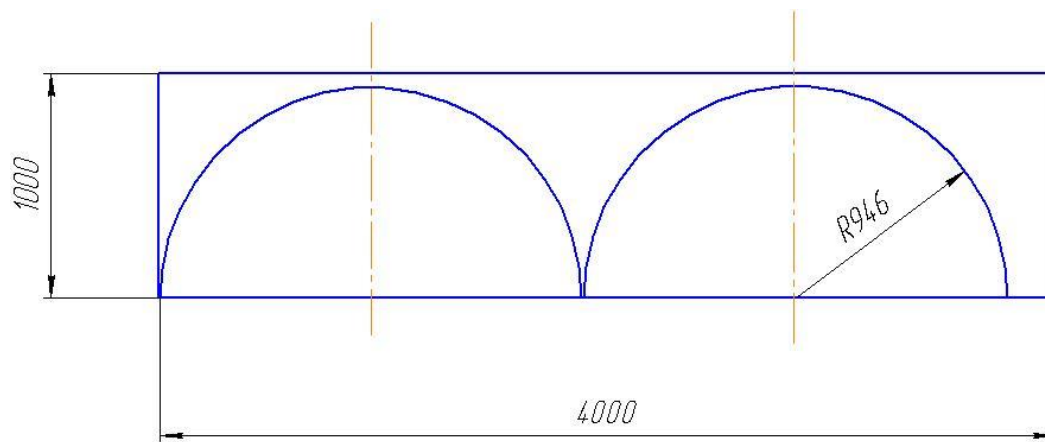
Ескіз розкрою заготовки днища на листі
